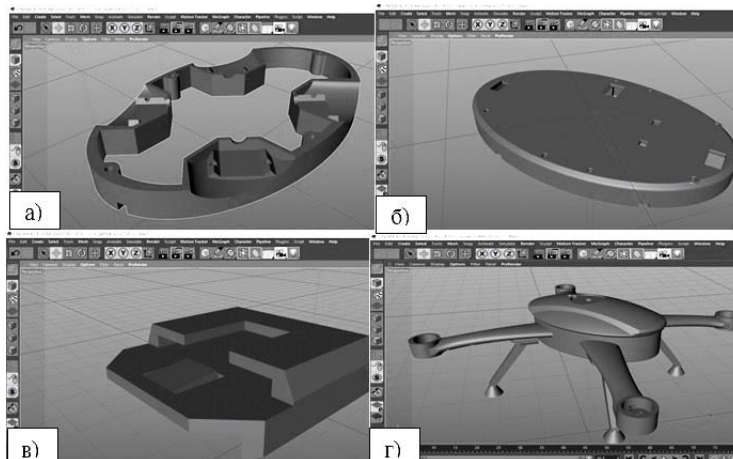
а) Основание для крепления рамы; б) Нижняя крышка корпуса БПЛА; в) Кронштейн для крепления шасси к раме; г) Сборочная 3D-модель
